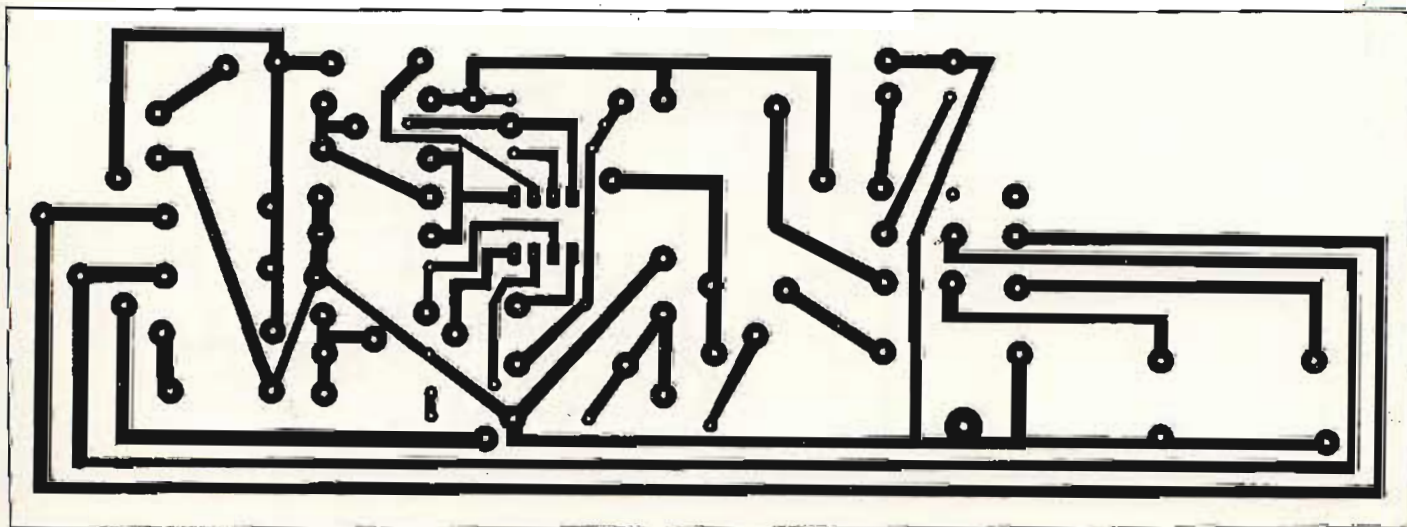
Disegno delle piste della basetta stampata su cui è montata la protezione elettronica.
